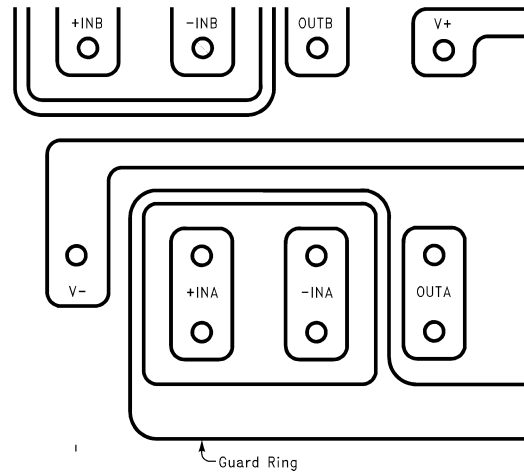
布局示例：在 PCB 布局中使用 LMC603x 防护环
